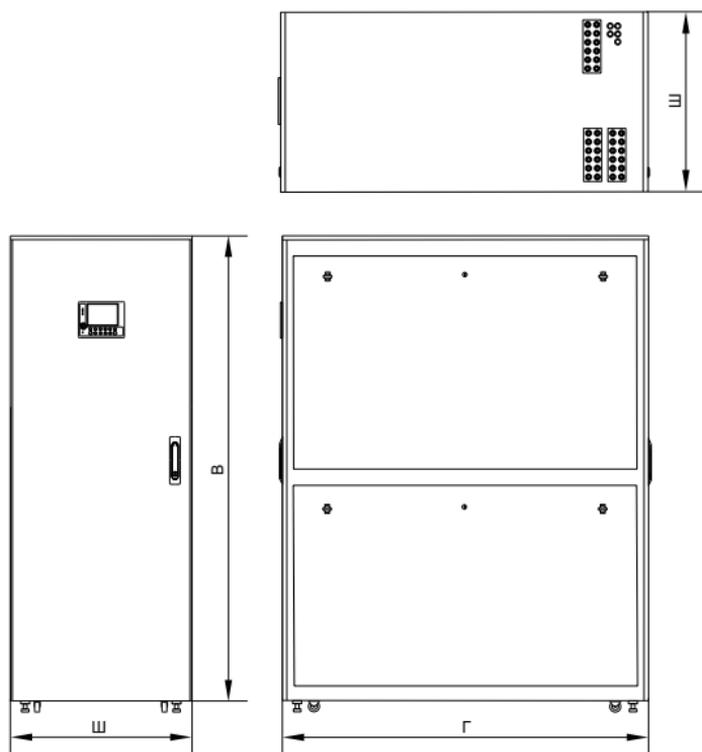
Габаритные размеры аппаратного шкафа КСОД серии DCI
